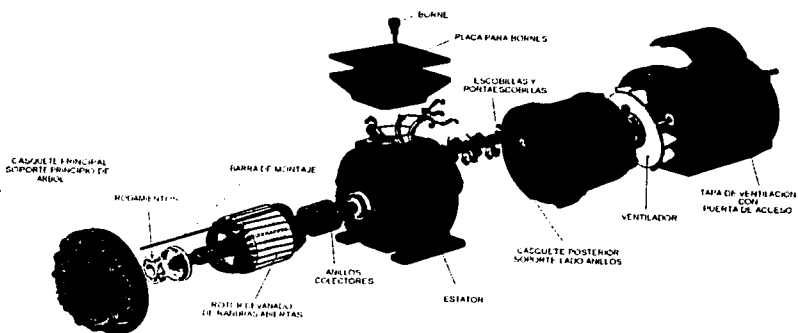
detalles de construcción de un motor típico de rotor devanado.
